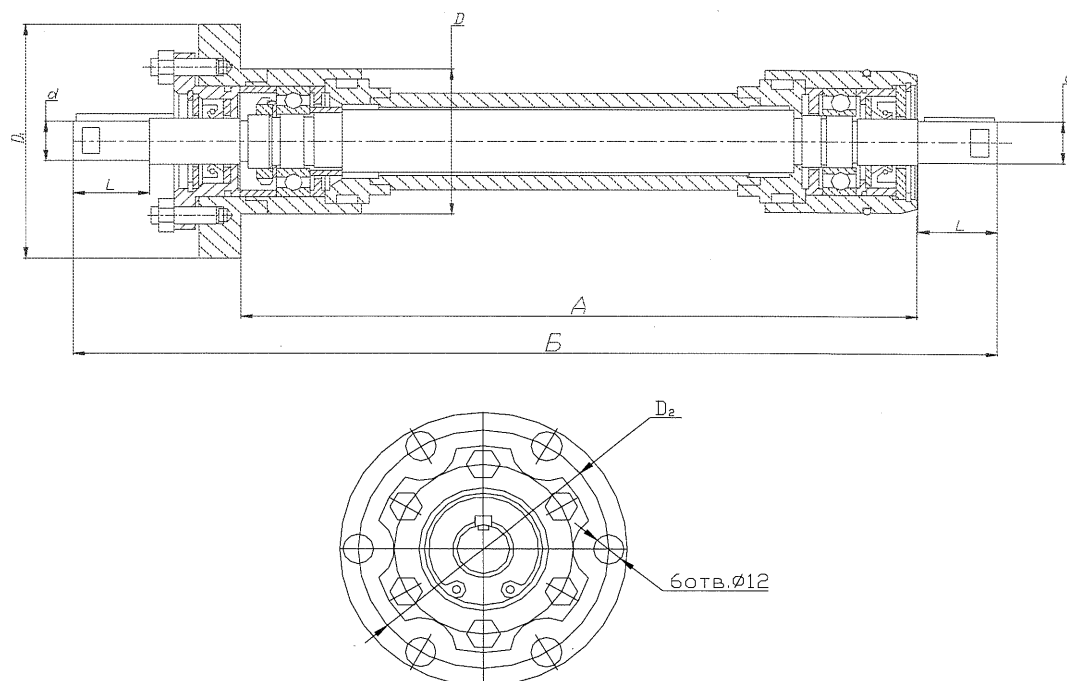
Габаритный чертеж штоковой проходки
